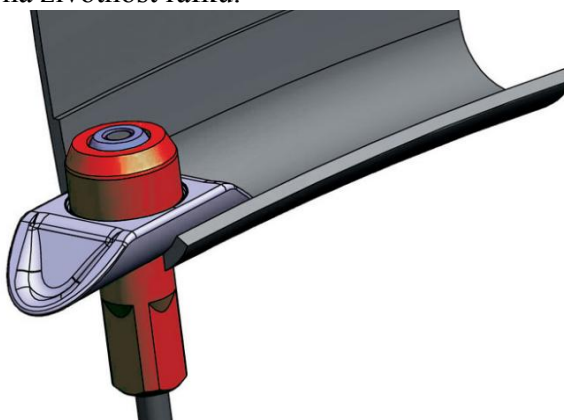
Ukázka nýtování na ráfku Remerx Master Disc [8]
